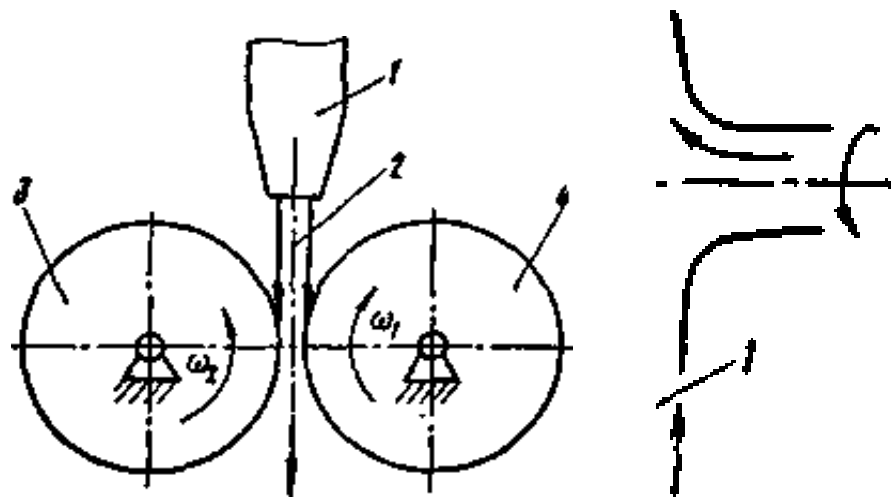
Одночасна струминна обробка циліндричних заготовок:
